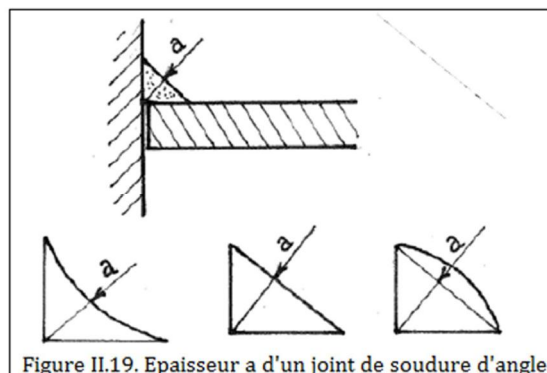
Epaisseur a d'un joint de soudure d'angle.
